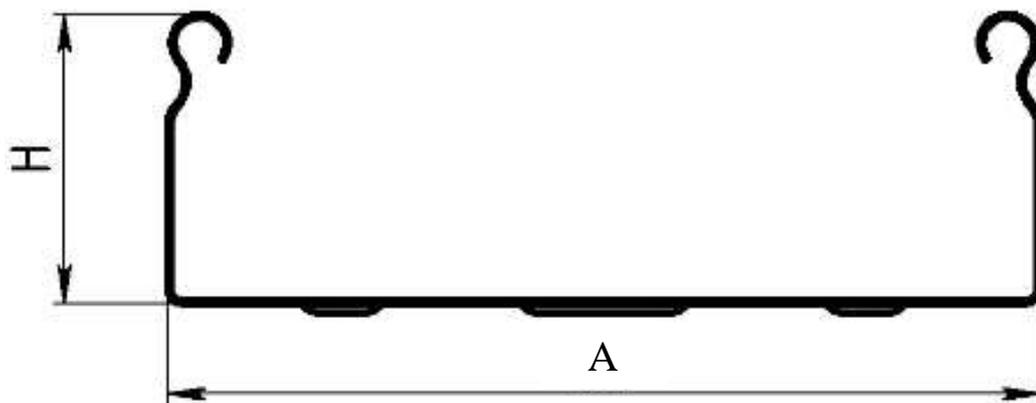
Лоток перфорированный с шириной полки 50, 100, 150, 200, 300, 400, 500, 600 мм и высотой стенок 50, 80, 100 мм
